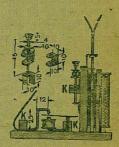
Детали вызывной кнопки и место ее установки. Здесь же даны размеры прерывателя зуммера.
